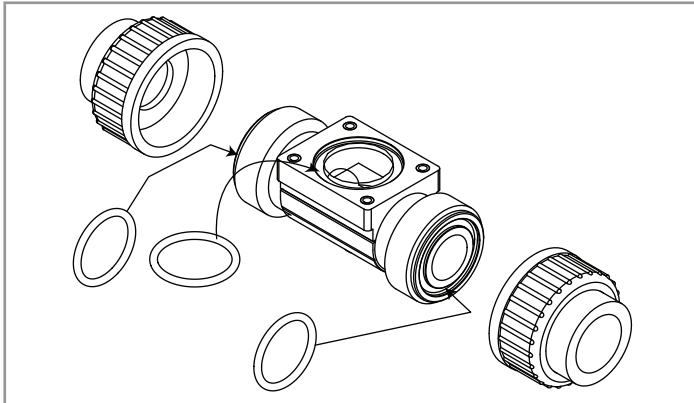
O-Ring-Dichtungen für Kunststoff-Fitting
